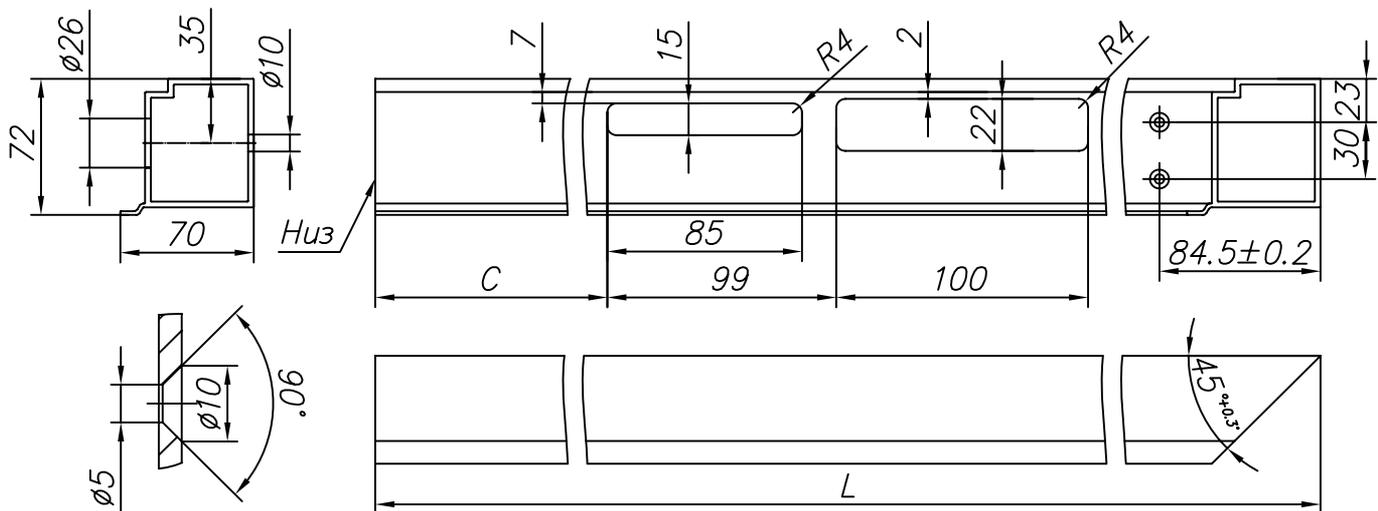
Изготовление столба притвора с пазом для автоматической защелки 118WE для калитки с перекладиной (открывание вправо)
